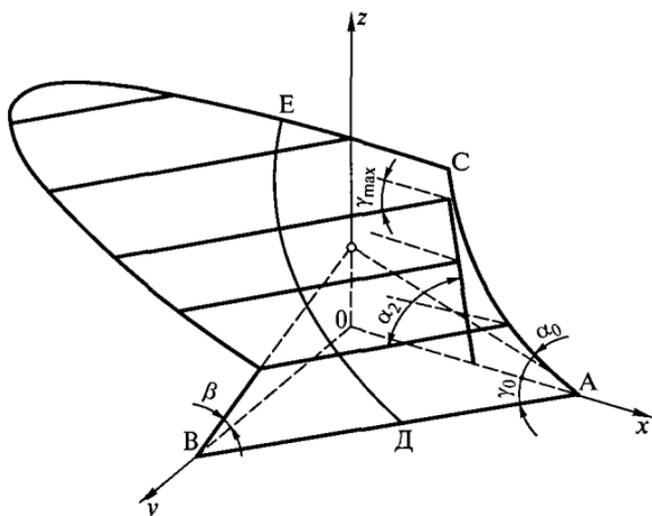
Схема образования рабочей поверхности корпуса плуга
